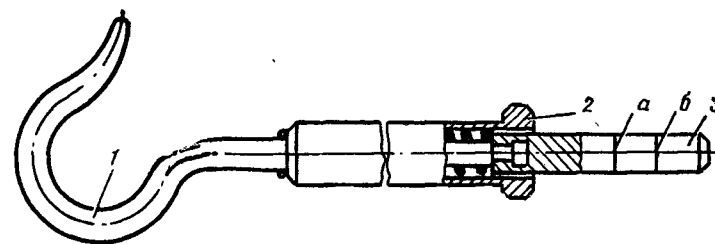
Прибор для проверки усилия спуска с боевого взвода пулемета ДШКМ:
